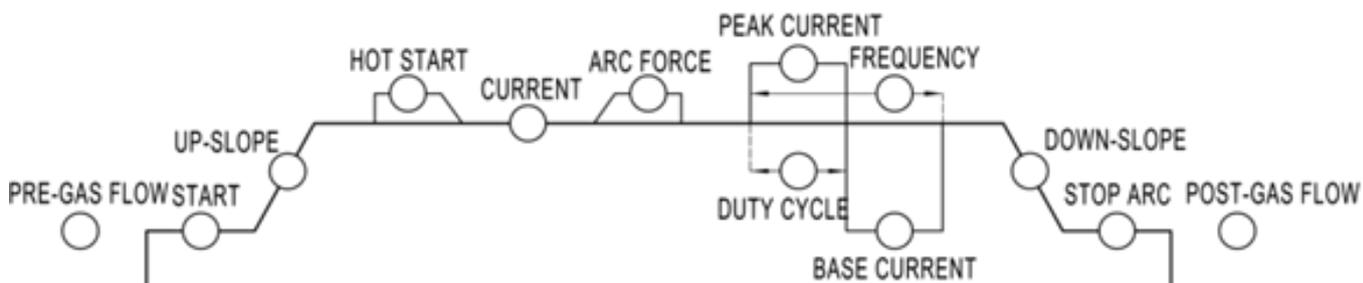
Параметр источника сварочного тока
